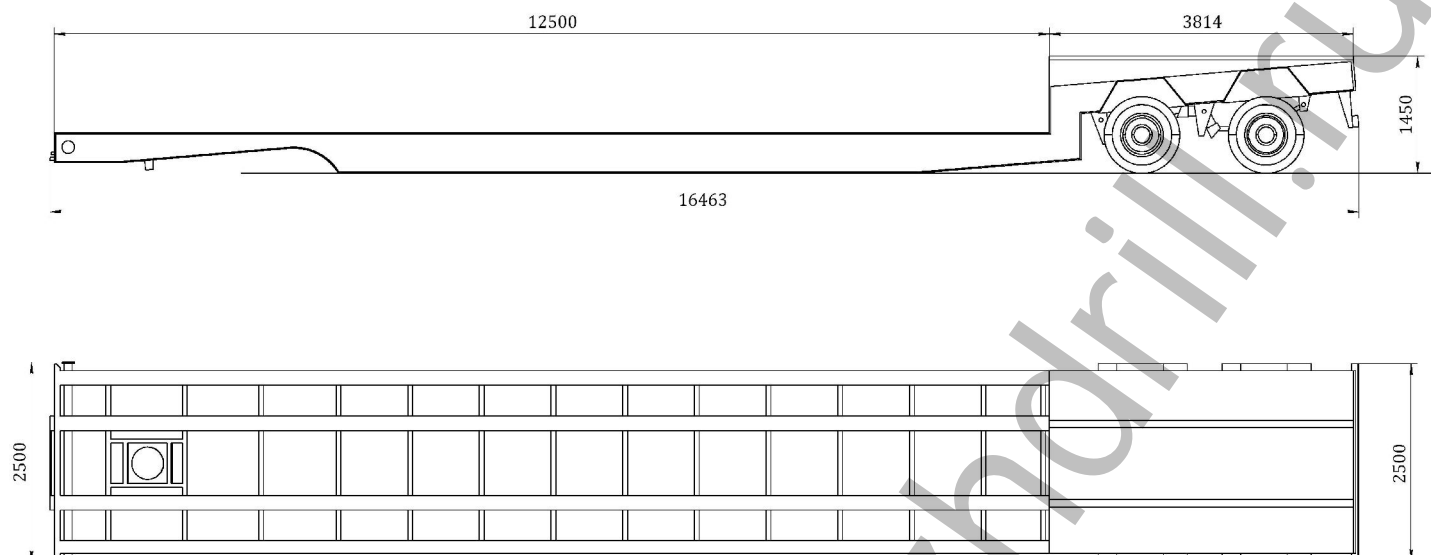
Общий вид полуприцепа 9420-0000010-01
